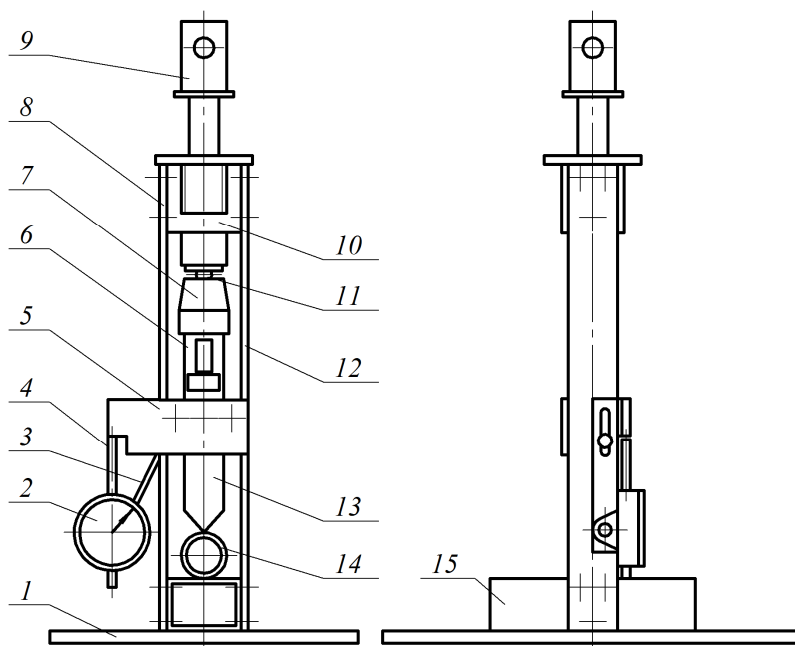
Конструкция силового режущего блока испытательного стенда
